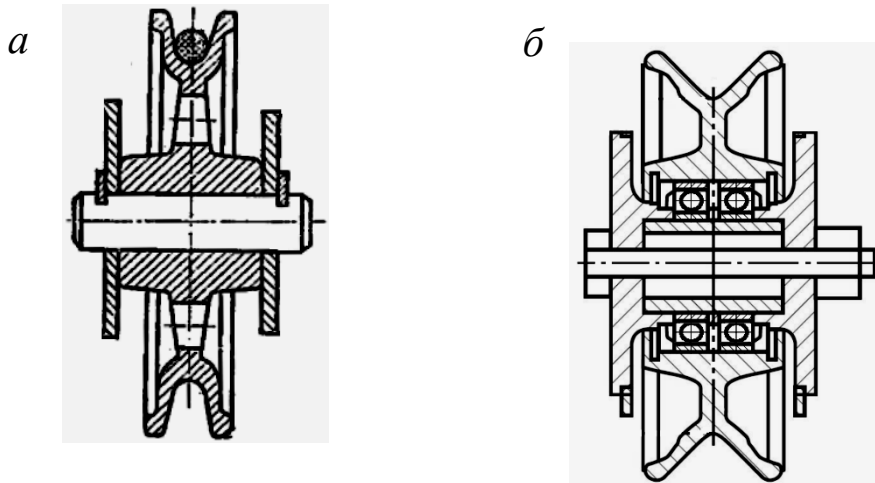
Блоки для канатів з підшипниками ковзання (а) і кочення (б)
